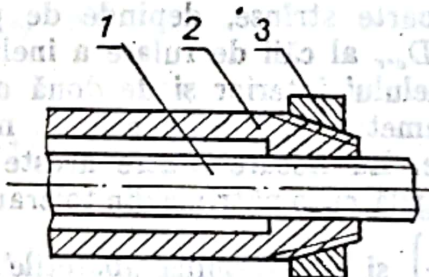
Lanț de dimensiuni cu compensator mobil periodic.
